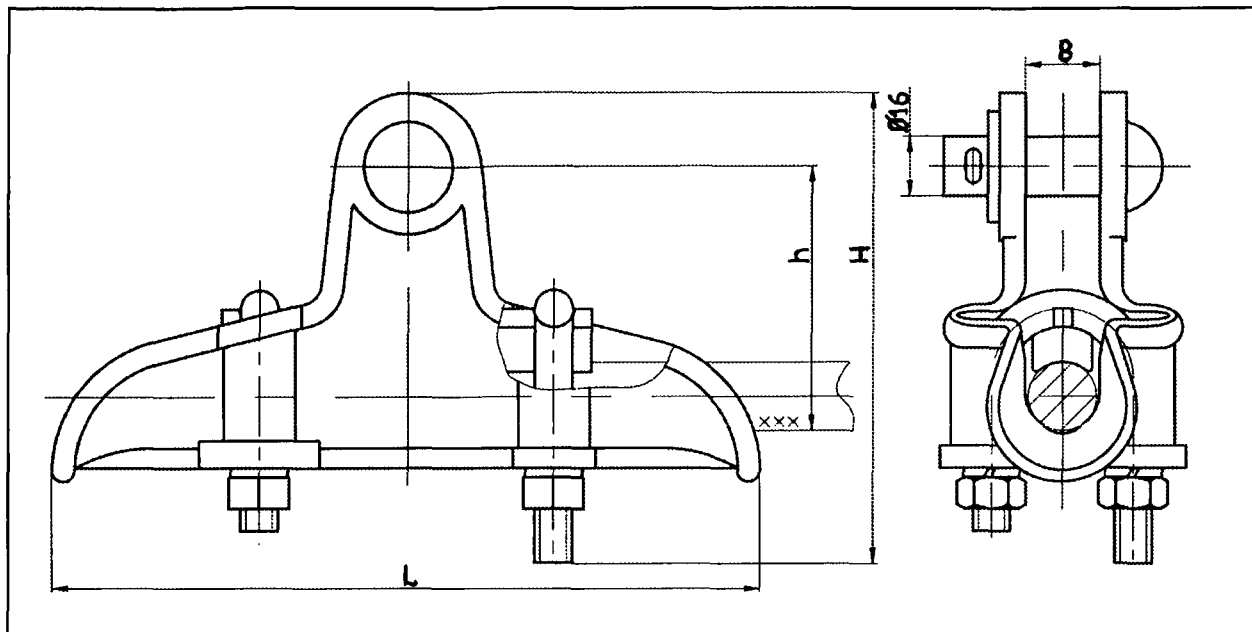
Внешний вид, конструкция и размеры зажимов ПГ-2-11У и ПГ-3-12У
